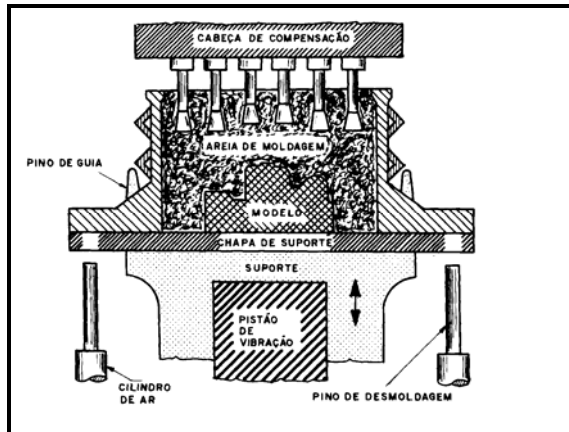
Máquina de Socamento por Impacto e Compressão
